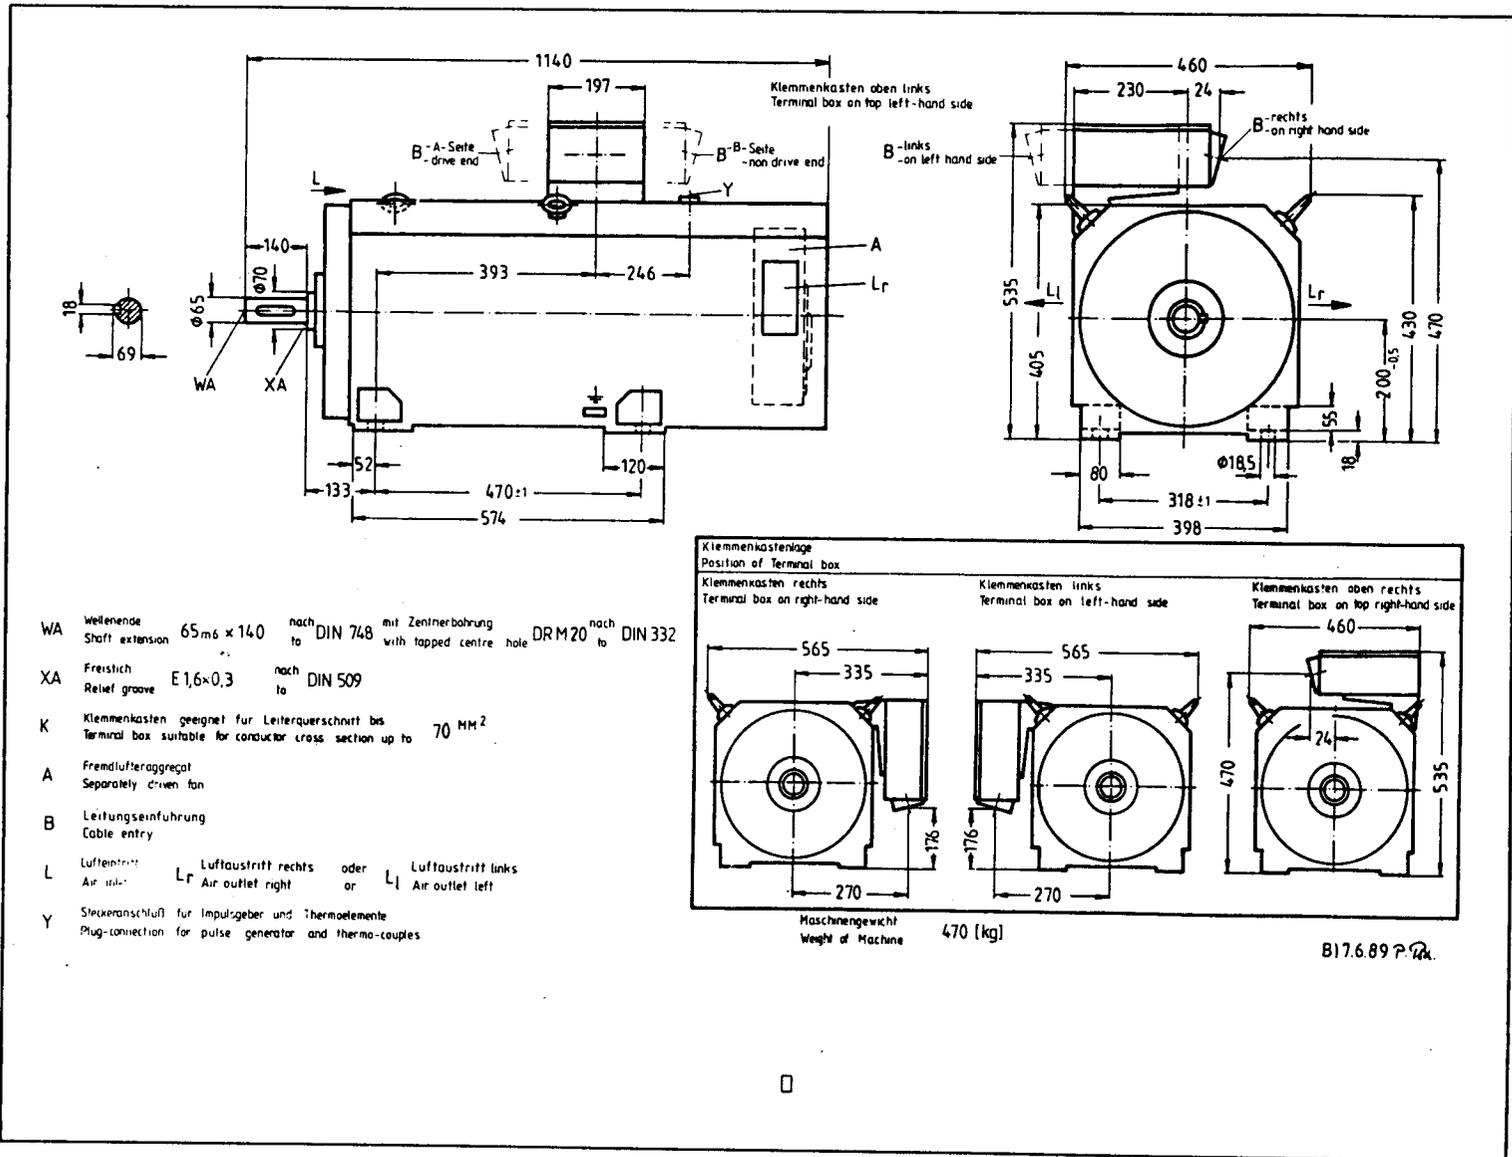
Maßblatt Drehstrommotor 1PH6 206-4C, Bauform IM B3 (Maße in mm, ohne Maßstab)
